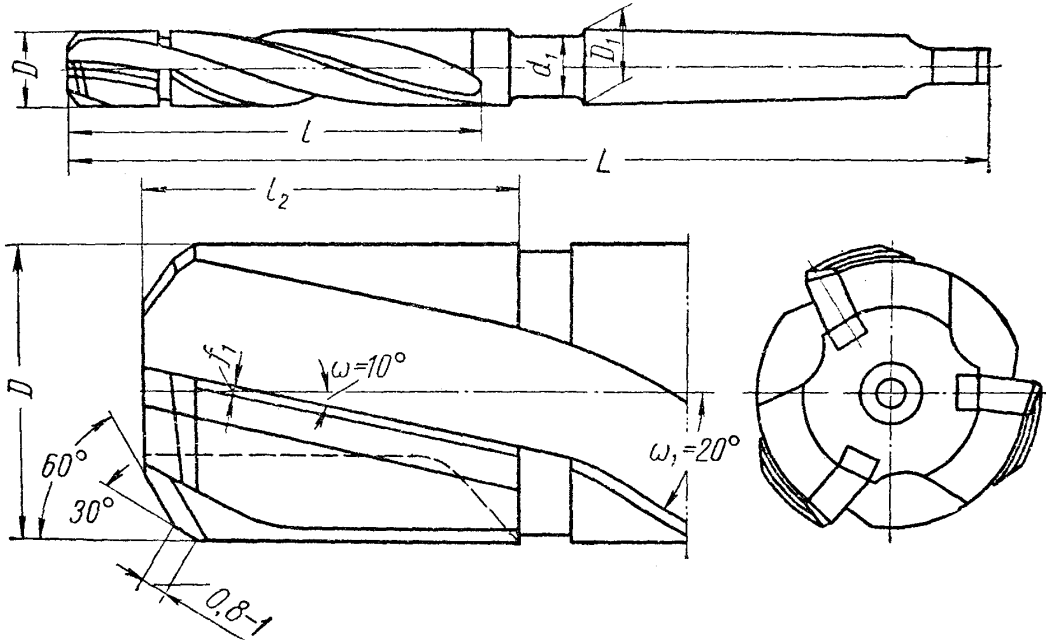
Цилиндрический хвостовой зенкер с пластинами из твердого сплава
